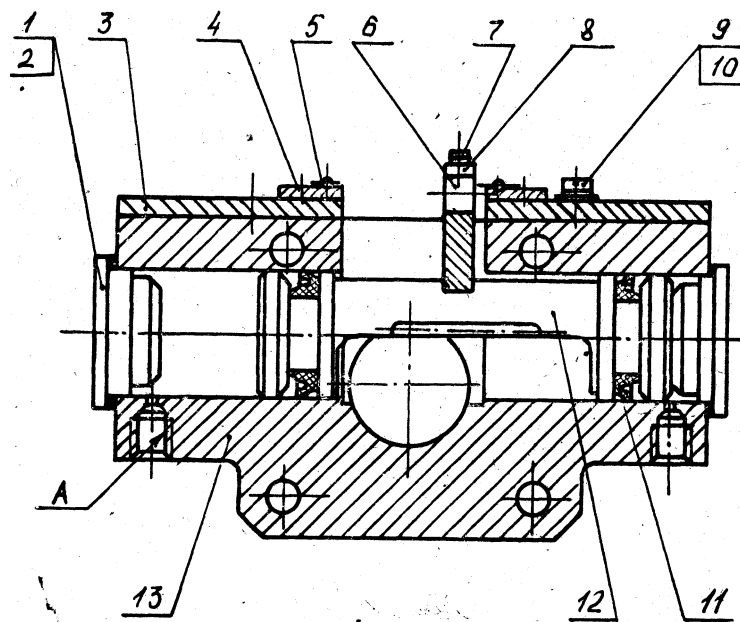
Механізм повороту: 1 – фланець; 2 – прокладка; 3 – планка; 4 – плата; 5 – магнітокерований контакт (КЕМ); 6 – магніт; 7 – гвинт; 8 – планка; 9 – гвинт; 10 – шайба пружинная; 11 – манжета; 12 – рейка; 13 – корпус.
